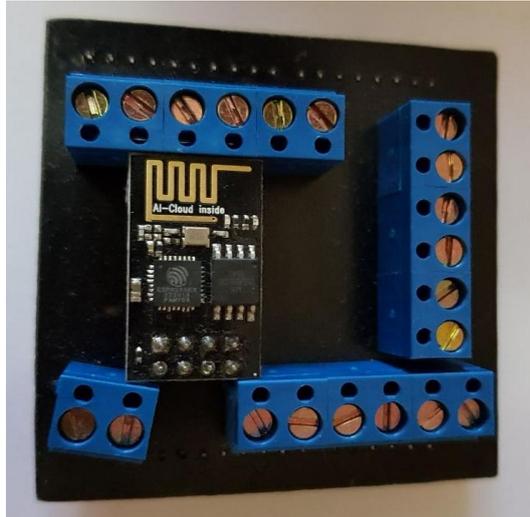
43: Módulo WiFi acoplado a la placa de circuito impreso
